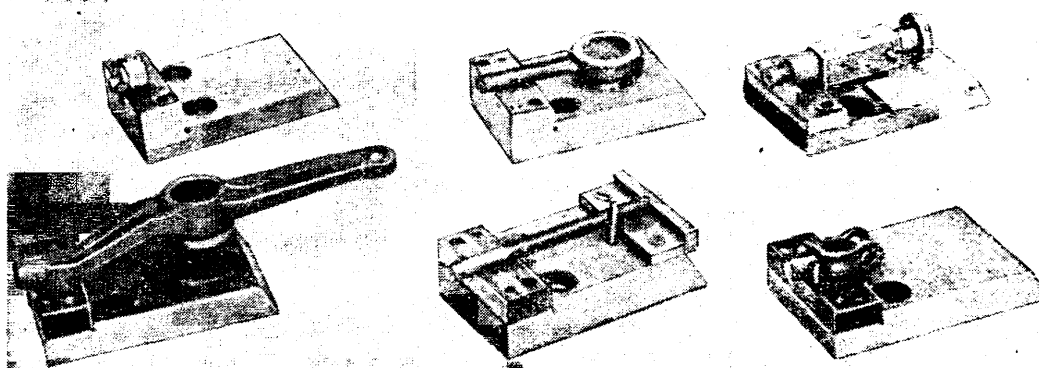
Сменные приспособления (без верхнего зажима) с установленными на них свариваемыми деталями
